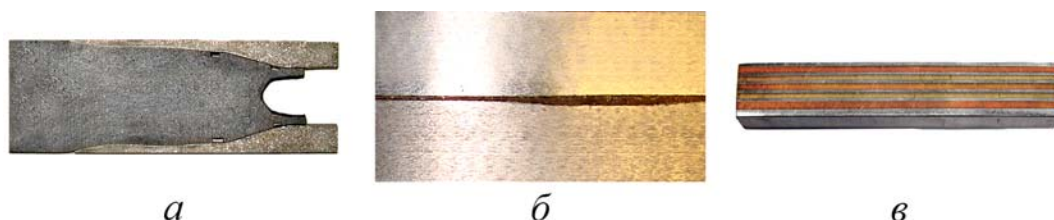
Багатошарові металеві композиції, виготовлені методом вакуумної термомеханічної обробки²⁴:
